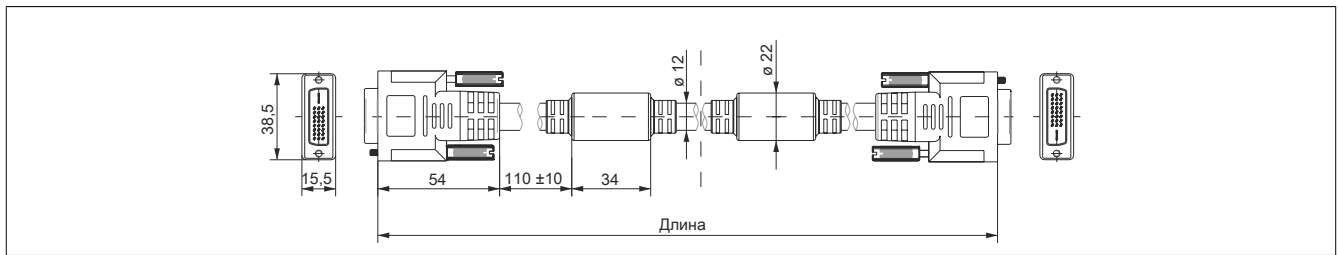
5CASDL.0xxx-03, аппаратная версия E0 и выше — размеры
